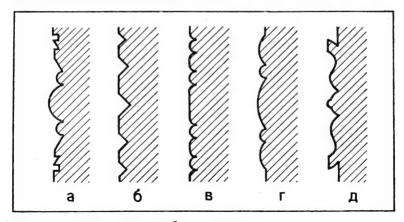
Основные типы резьбы по дереву: а — геометрическая резьба с углубленным рисунком; б — контурная резьба; в с заоваленными контурами; г — с подушечным фоном; д — с подобранным фоном
